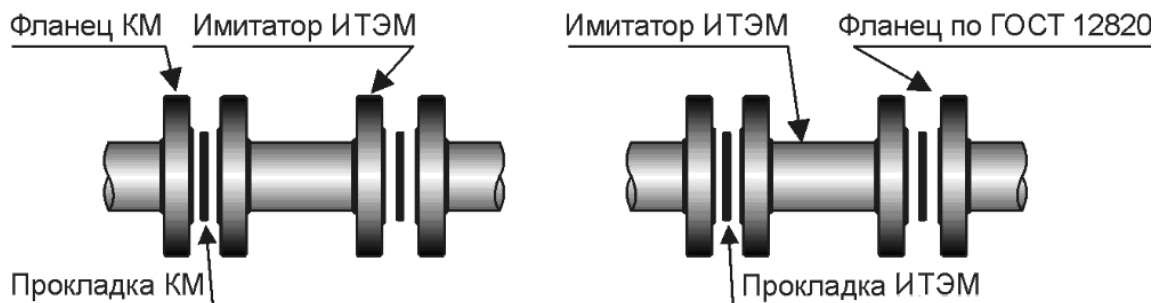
Установка габаритного имитатора ИТЭМ
